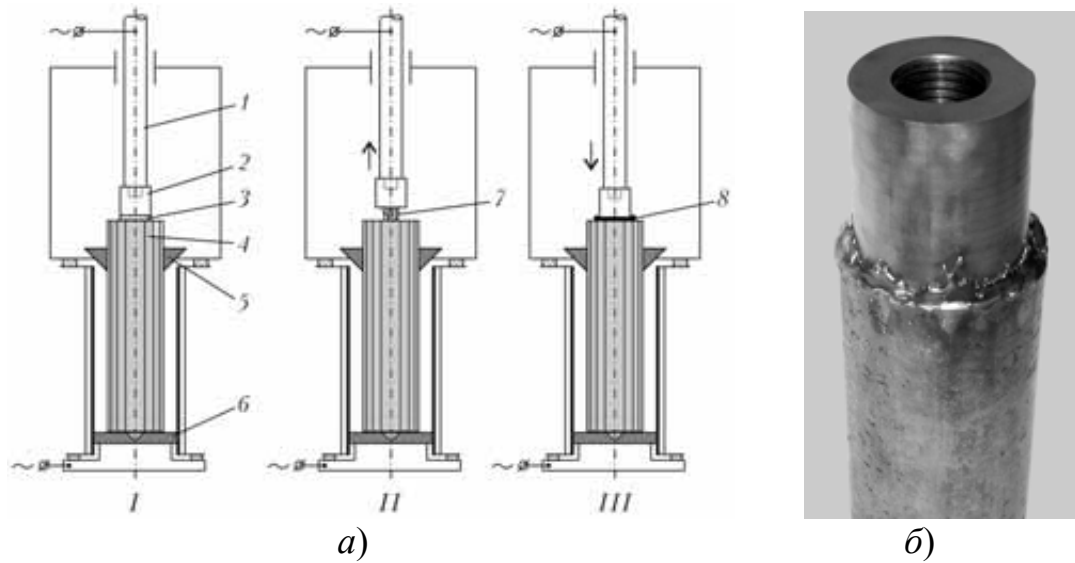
Схема приварювання інвентарної головки до витратного електроду (а) і вигляд зварного з'єднання (б) (I – нагрівання електричним струмом поверхонь, що з'єднуються; II – оплавлення поверхонь електричною дугою; III – осадка): 1 – шток вертикального переміщення електроду; 2 – інвентарна головка; 3 - струмопровідний прошарок; 4 - витратний електрод; 5, 6 – центруючі втулки; 7 – електрична дуга; 8 – зварне з'єднання
